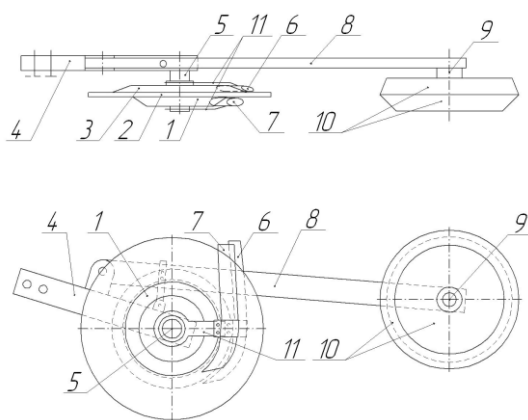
Комбинированный однодисковый сошник с двухсторонними ребордами-бороздкообразователями с разными диаметрами и нулевым углом атаки дисков: 1 – уплотнители; 2 – плоский диск; 3 – уплотнитель; 4 – корпус; 5 – ось; 6 – семянаправитель; 7 – туконаправитель; 8 – поводок; 9 – ось; 10 – прикатывающий каток; 11 – пластины
